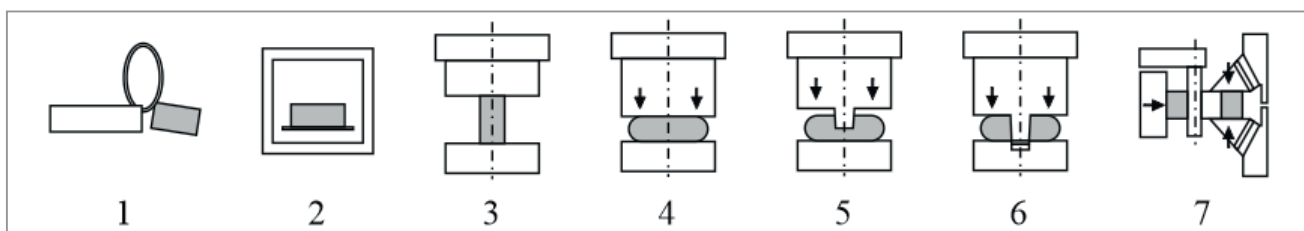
Технологический процесс изготовления кольцевых заготовок:
